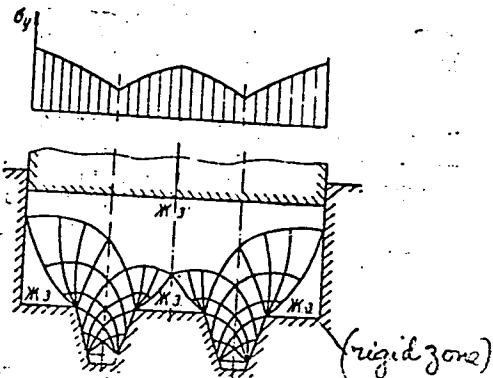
Поля линий скольжения при штамповке в закрытых штампах и эпюры нормальных напряжений (Ж.з. — жесткая зона).
